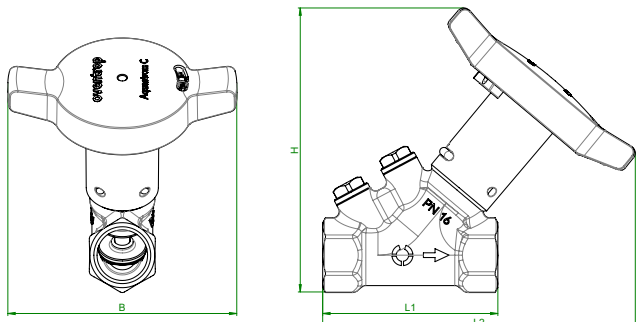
Dimensiones vista lateral / vista frontal rosca interior sin accesorios
